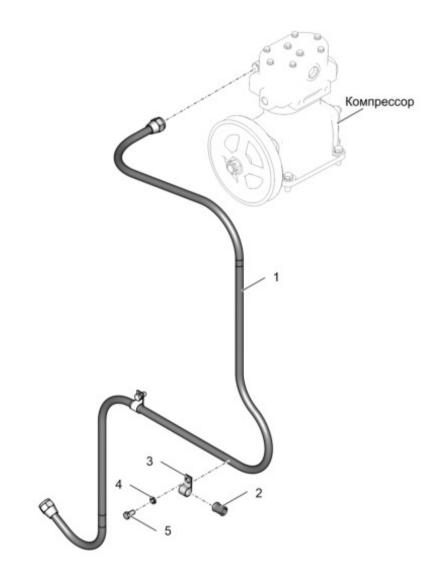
4320Х-3506180 Установка трубки к компрессору
